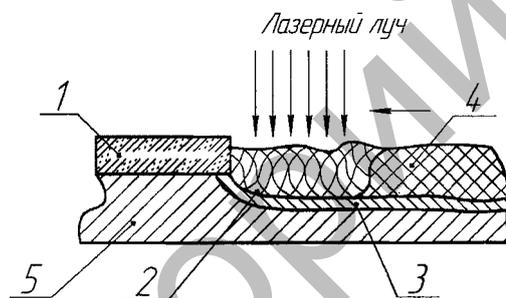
Схема лазерной наплавки: 1 – обмазка (материал будущей наплавки); 2 – расплав; 3 – зона лазерной закалки; 4 – наплавленный слой; 5 – основной металл
